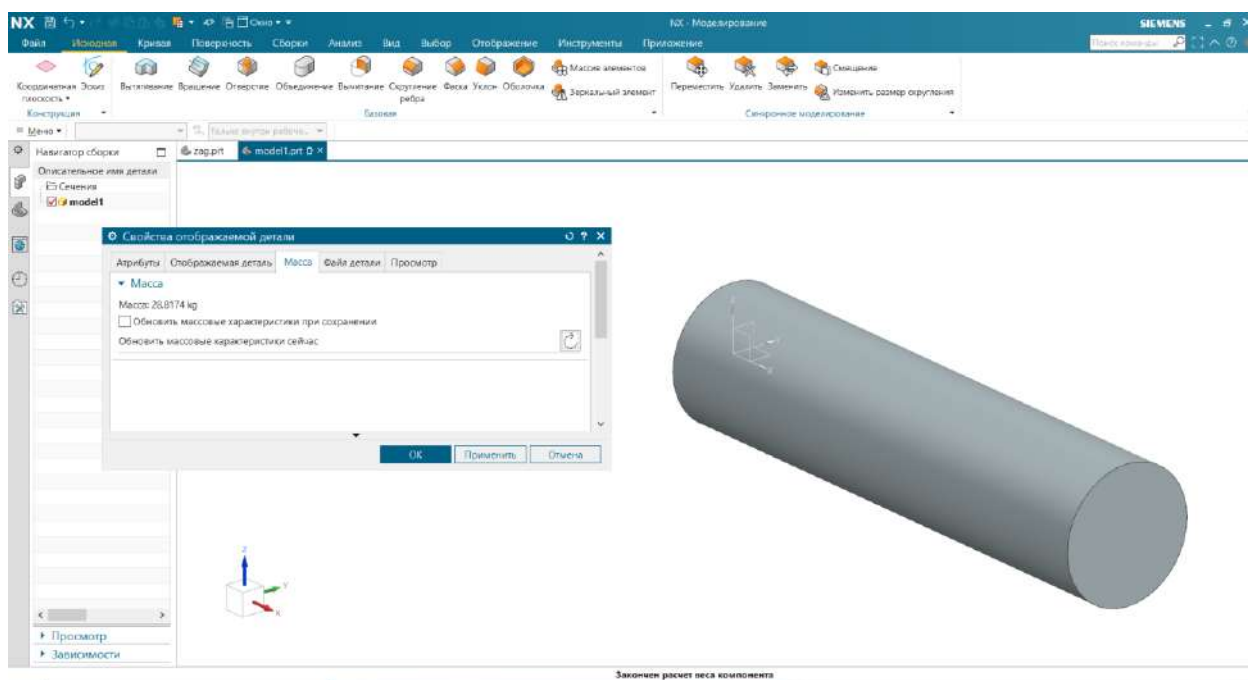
Визначення ваги заготовки отриманої з прокату
